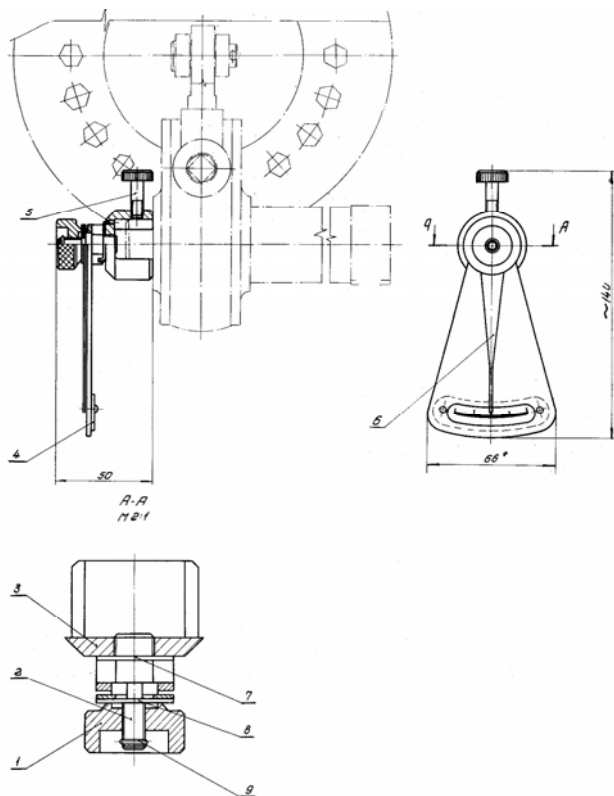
Конструкция прибора для проверки тормозов с пневматическим приводом
